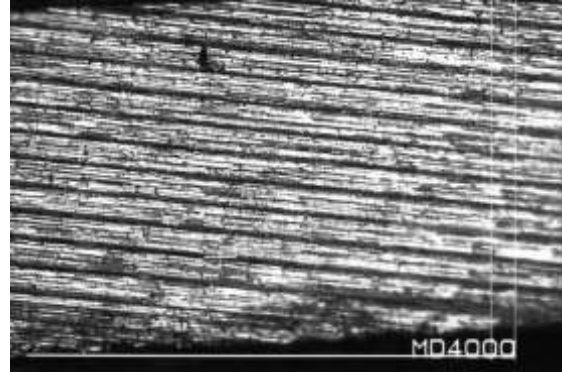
b. Das Gewinde des Messing -Teils nach zweiseitiger Ultraschalleinwirkung.
